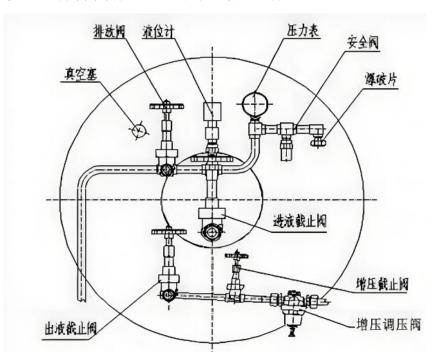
焊接绝热气瓶(液氧)设备简图
